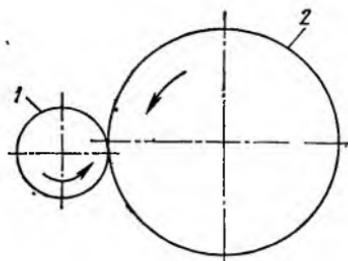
Принцип действия устройства для фрезерования резьбы и obtачивания многогранников: 1 — заготовка; 2 — фреза или резцовая головка
